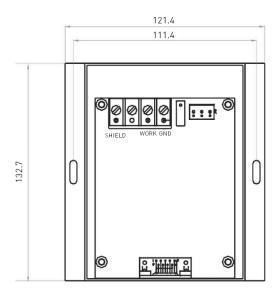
Габаритные размеры контроллера PTHC-IHS
